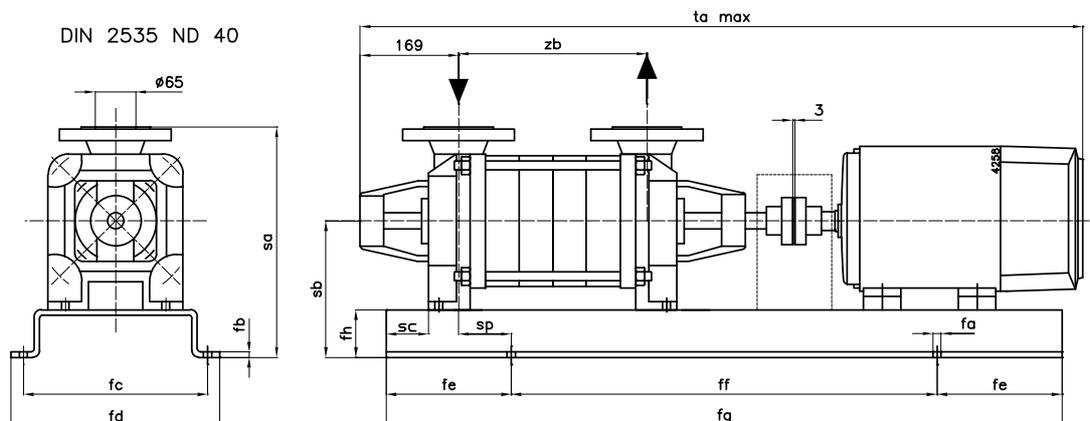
Dimensioni pompa con motore MCHZ(S) 16.
